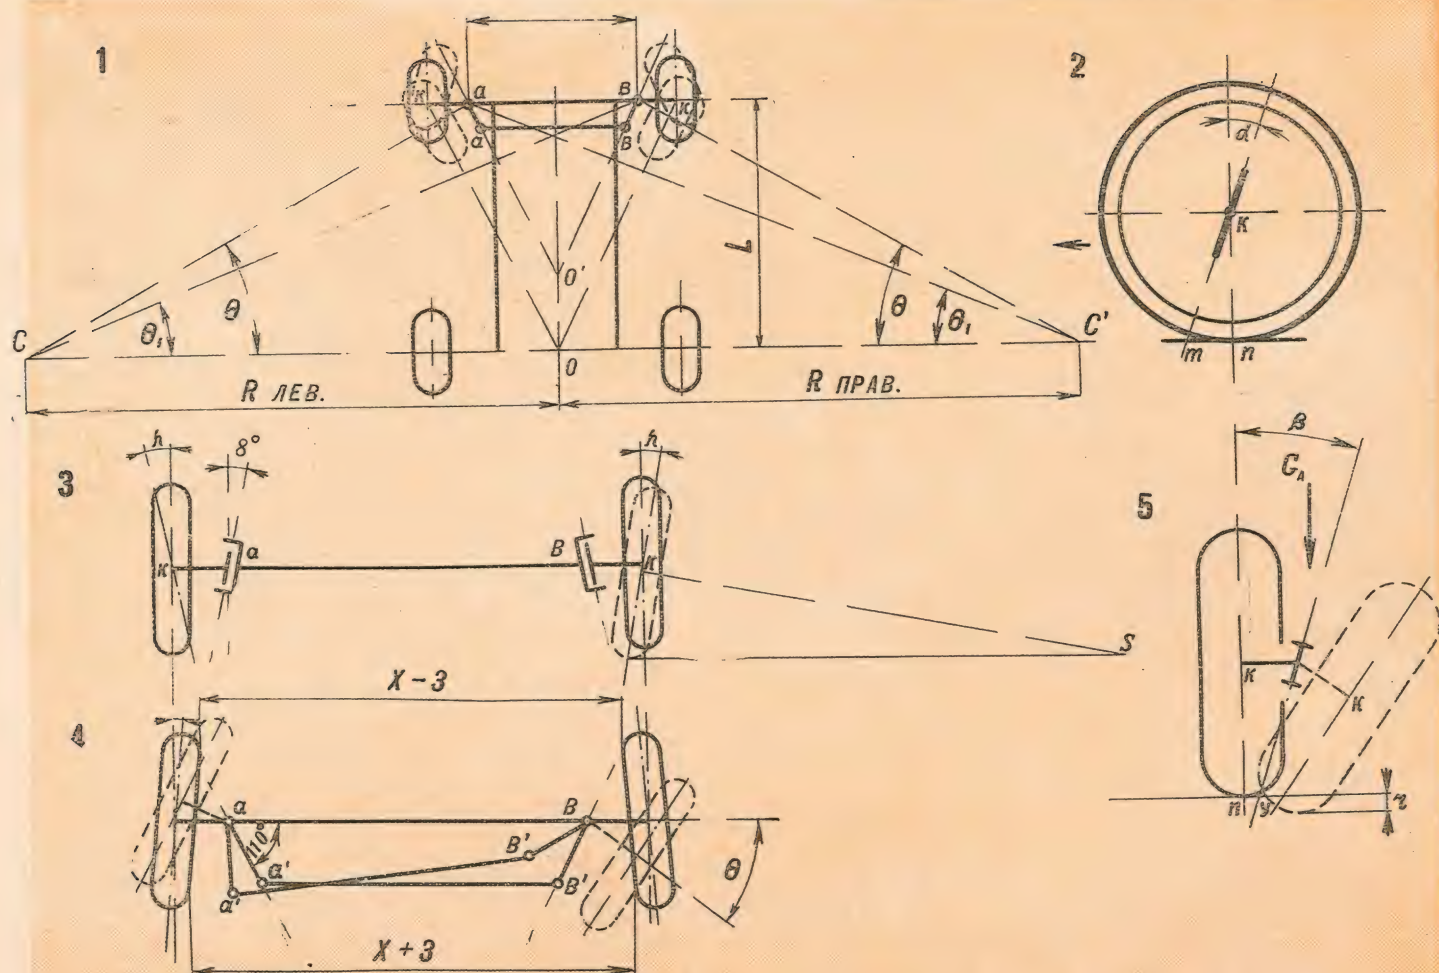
Установочные углы управляемых колес и кинематика рулевого привода:
